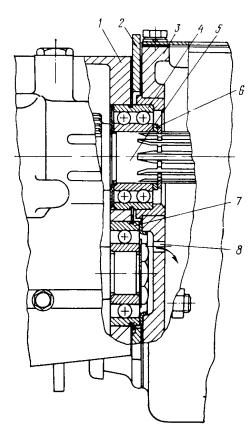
Установка заднего подшилника и ведомого вала в картер коробки передач автомобиля УАЗ-452: 1 — картер коробки передач; 2 — пластина крепления разлаточной коробки и коробки передач; 3 — картер раздаточной коробки; 4 — задний подшининк ведомого вала; 5 — ведомый вал; 6 — упорное кольцо; 7 — задний подшининк промежуточного вала; 8 — отверстие для слива масла
